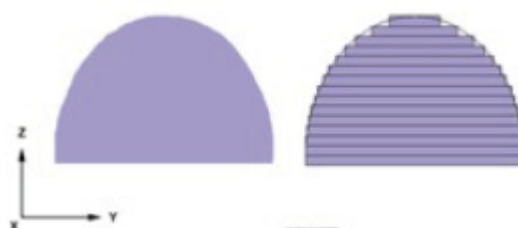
Defeito de "degraus" ou "escada"[23]
